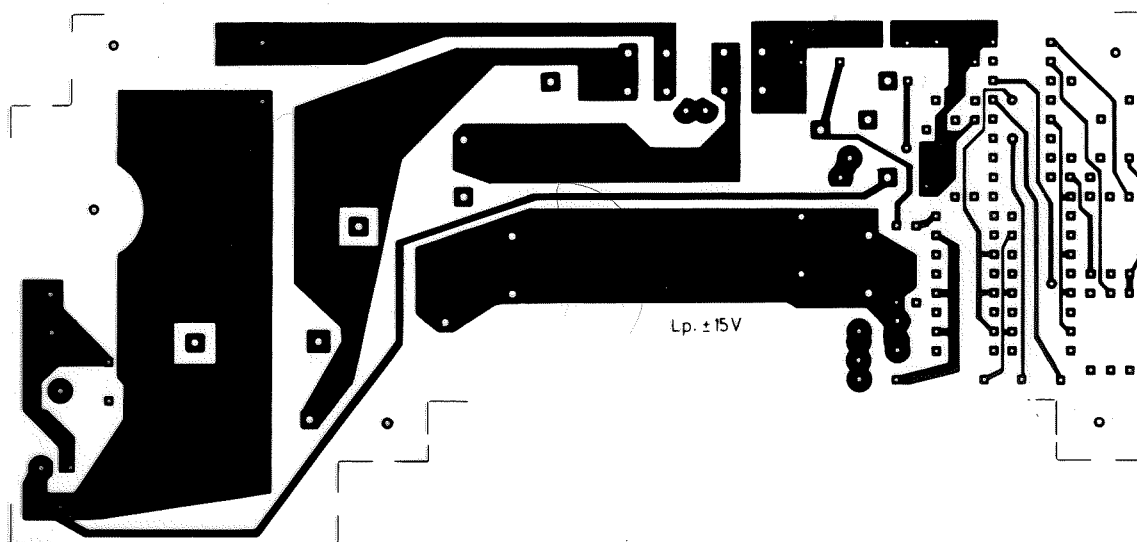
/13.4-11: Soldeerzijde 15-V-print.
